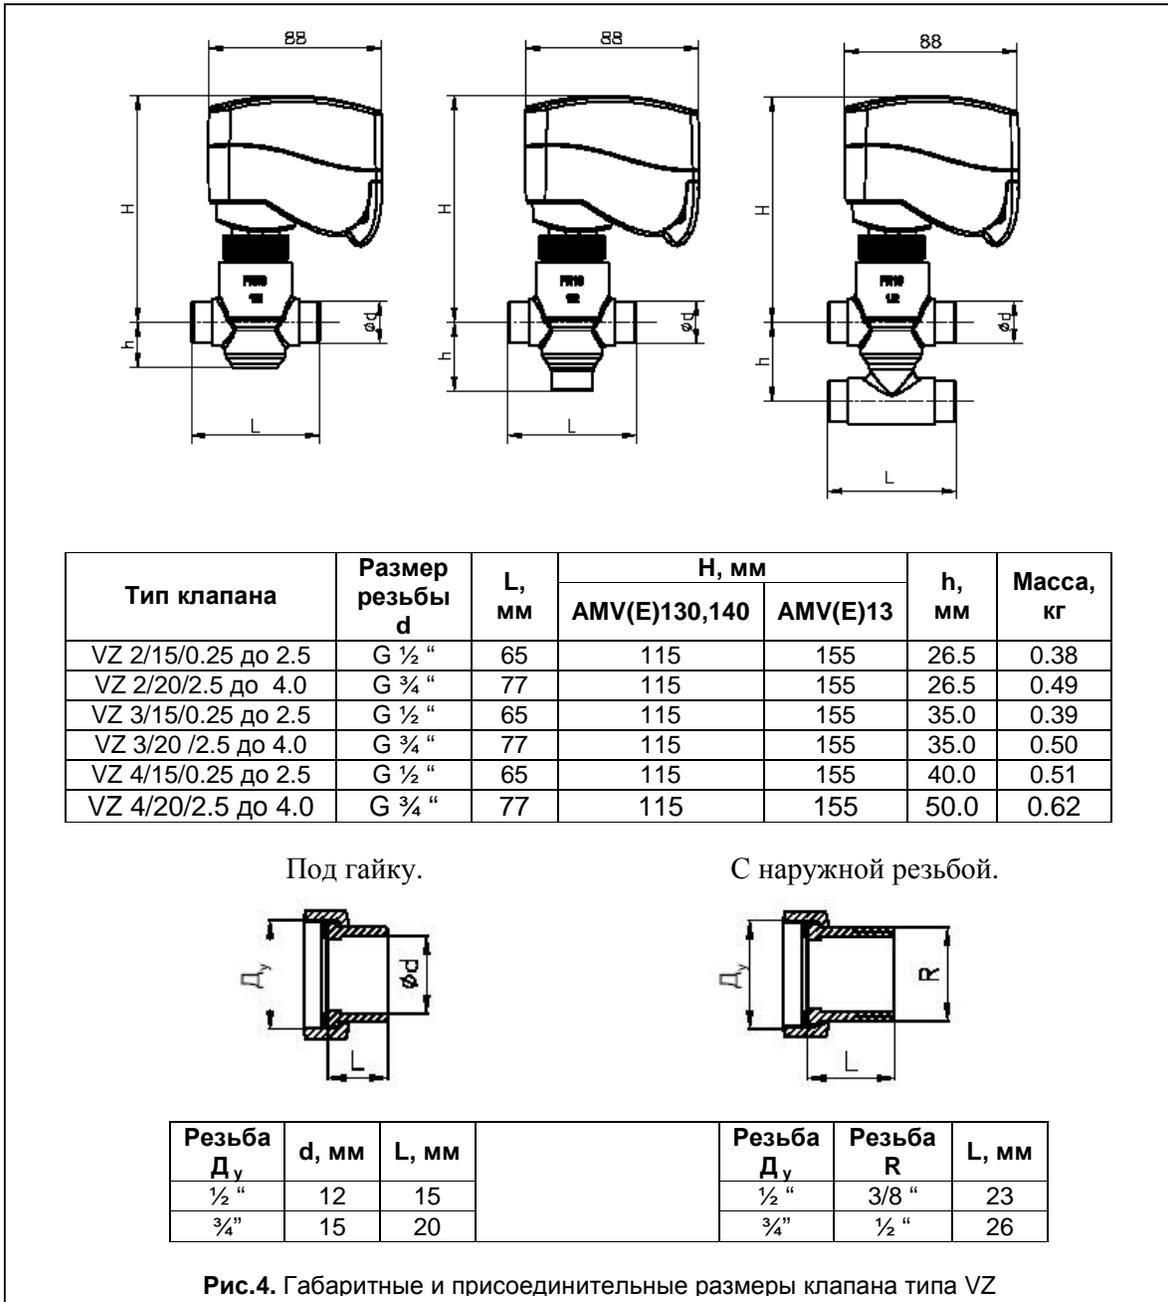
Габаритные и присоединительные размеры клапана типа VZ
